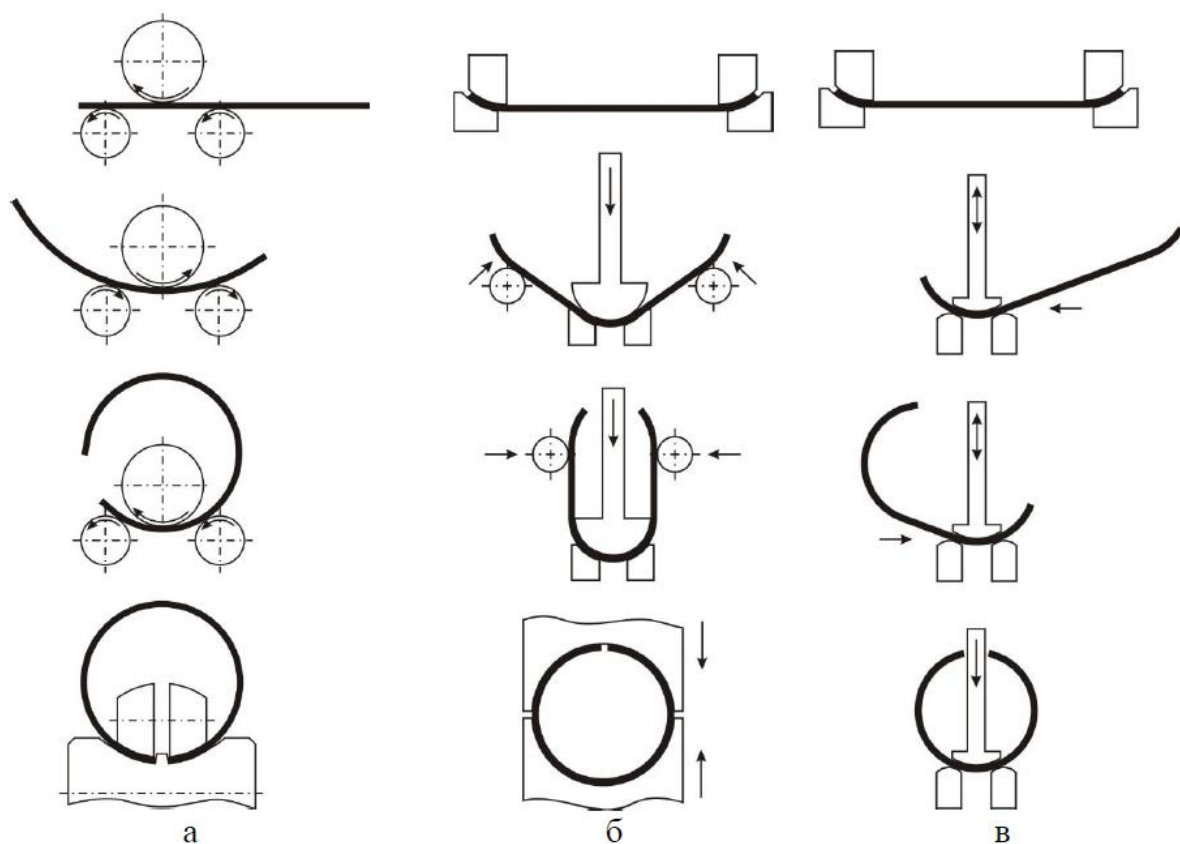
Способы формовки трубной заготовки для прямошовных сварных труб большого диаметра:
